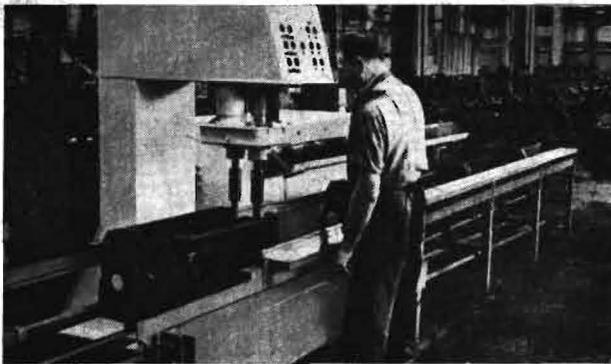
Hydraulischer Mehrschrauber in der Motorenhäuser-Vormontage
